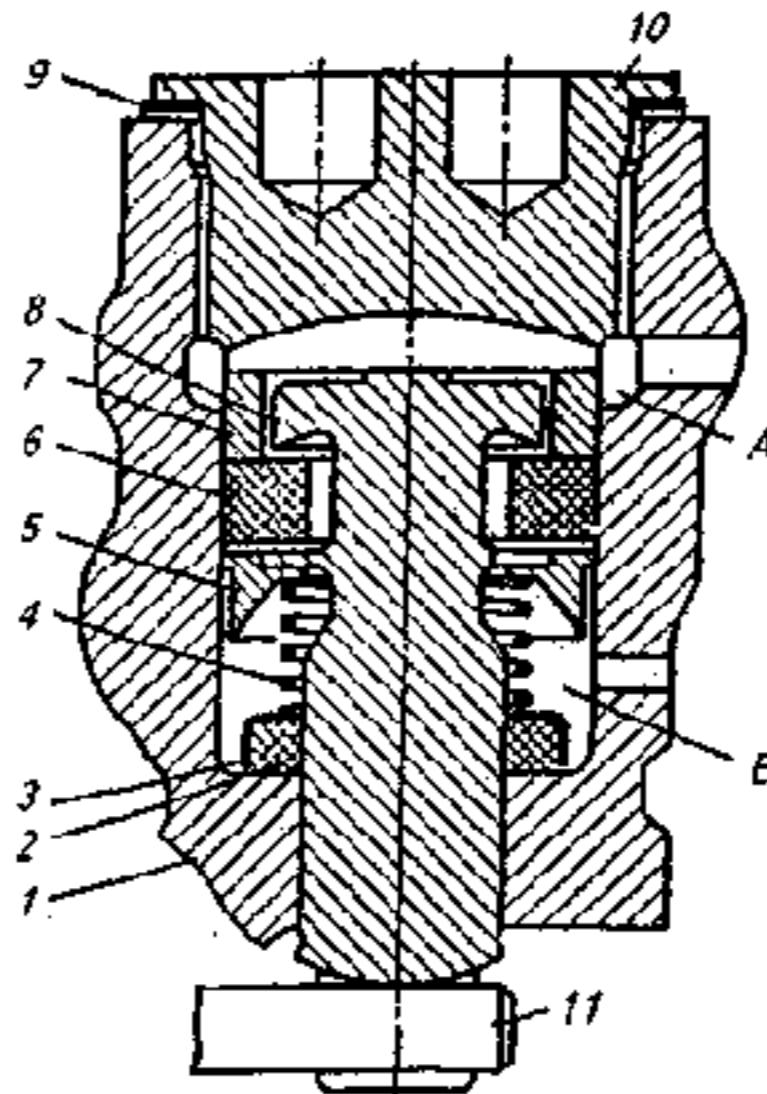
Регулятор давления автомобиля ВАЗ-2121: А, Б- полости регулятора; 1 — корпус; 2—уплотнительное кольцо; 3— обойма; 4— пружина; 5—тарелка; 6 — резиновый уплотнитель; 7-распорная втулка; 8— поршень; 9—прокладка; 10— пробка; 11 — торсион привода регулятора
